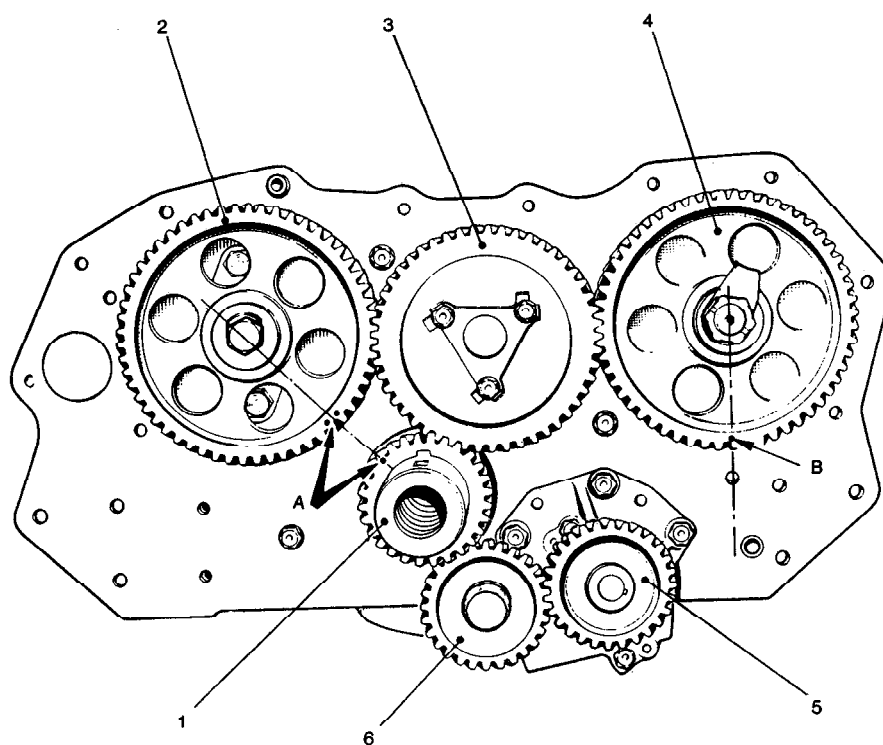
Engranes de sincronización: 1 engrane del cigüeñal, 2 engrane del árbol de levas, 3 engrane intermedio (loco), 4 engrane de mando de bomba de inyección, 5 engrane de mando de bomba del aceite, 6 engrane intermedio, A marcas para sincronización de válvulas, B marcas para sincronización de la bomba de inyección
